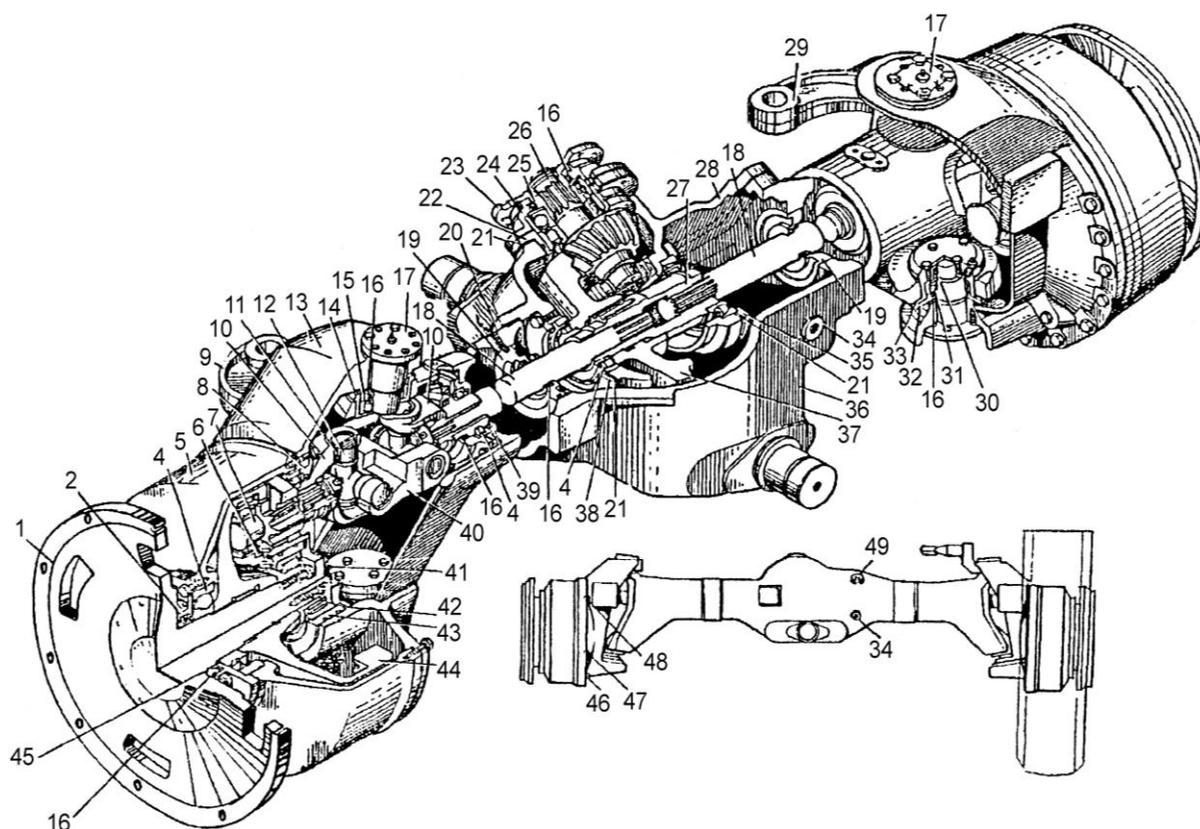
Передний мост: 1 – ступица; 2 – уплотнительное кольцо; 4 – подшипник; 5 – корпус бортового редуктора; 6 – вкладыш; 7, 26 – вал-шестерни; 8, 24, 38, 41 – крышки подшипников; 9, 29 – кронштейны крепления поперечной тяги; 10 – вилка кардана; 11 – игольчатый подшипник; 12 – крестовина кардана; 13 – поворотный кронштейн; 14, 39, 43 – корпуса подшипников; 15, 32 – корпуса сальников; 16 – манжета; 17, 30 – пальцы; 18 – полуось; 19 – корпус манжеты; 20 – стопорный винт; 21 – регулировочные прокладки; 22, 33 – стаканы; 23 – фланец; 25 – маслоотражательная шайба; 27 – втулка; 28 – кронштейн главной передачи; 31 – упорный подшипник; 34 – контрольная пробка; 35 – крышка; 36 – балка; 37 – коническая шестерня; 40 – промежуточное звено кардана; 42 – прокладка; 44 – шестерня с внутренним зацеплением; 45 – втулка; 46 – сливная пробка; 47, 49 – пробки заправочных отверстий; 48 – сапун
